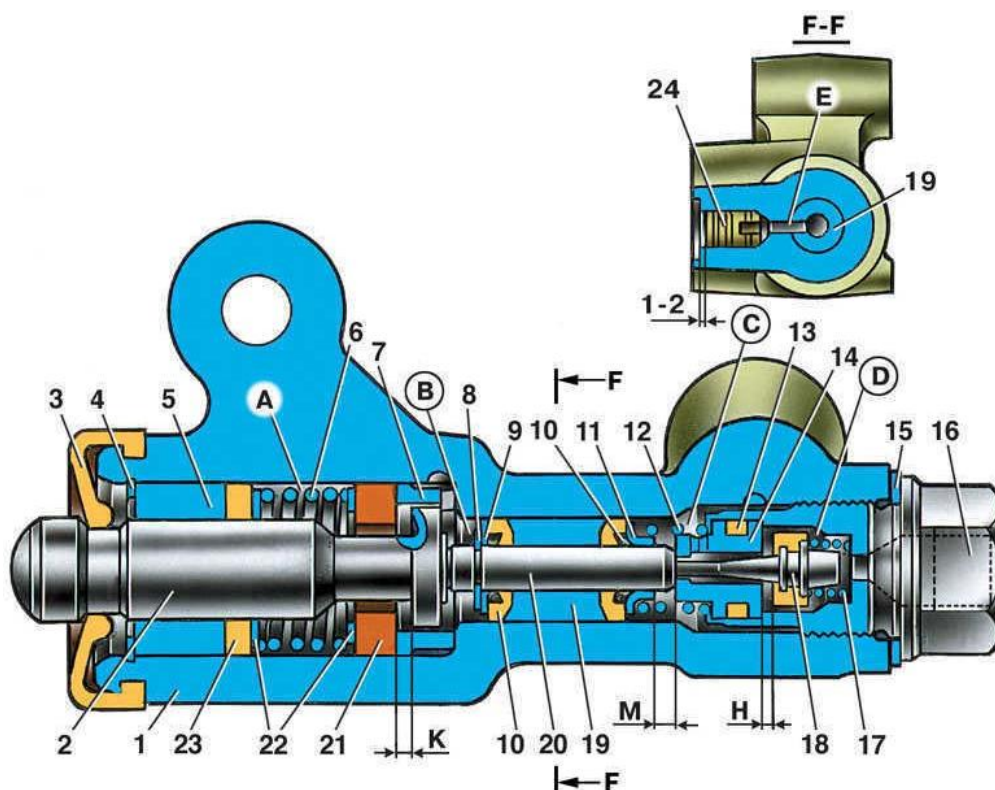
Регулятор тиску гальм автомобіля ВАЗ 2110: 1 - корпус регулятора тиску гальм; 2 - поршень; 3 - захисний ковпачок; 4, 8 - стопорні кільця; 5 - втулка поршня; 6 - пружина поршня; 7 - втулка корпуса; 9, 22 - опорні шайби; 10 - ущільнювальні кільця штовхача; 11 - опорна тарілка; 12 - пружина втулки штовхача; 13 - кільце ущільнювальне сидла клапана; 14 - сидло клапана; 15 - ущільнювальна прокладка; 16 - пробка; 17 - пружина клапана; 18 - клапан; 19 - втулка штовхача; 20 - штовхач; 21 - ущільнювач головки поршня; 23 - ущільнювач штока поршня; 24 - заглушка; А, D - камери, з'єднані з головним циліндром; В, С - камери, з'єднані з колісними циліндрами задніх гальм; К, М, Н - зазори; Е - дренажний отвір.
